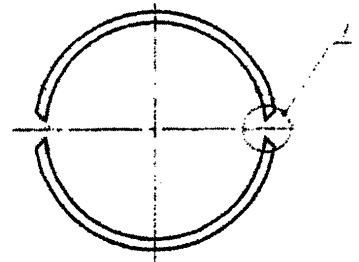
Разделка кромок полуфлэнгов под сварку
